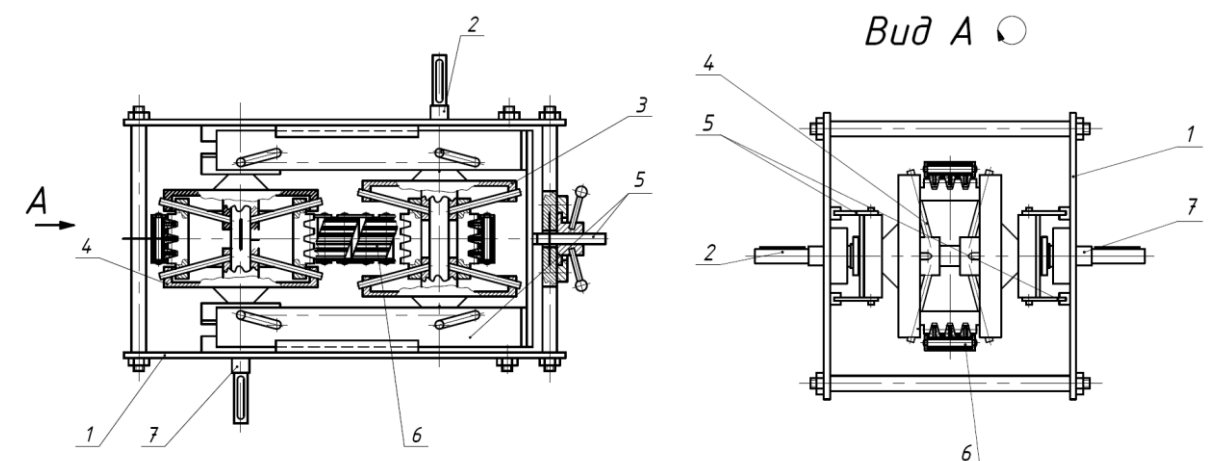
Вариатор с поликлиновым ремнем: 1 – корпус; 2 – ведущий вал; 3 – ведущий составной шкив; 4 – ведомый составной шкив; 5 – механизм регулирования передаточного отношения в виде плоского многопоточного кулачка; 6 – поликлиновый ремень; 7 – ведомый вал
